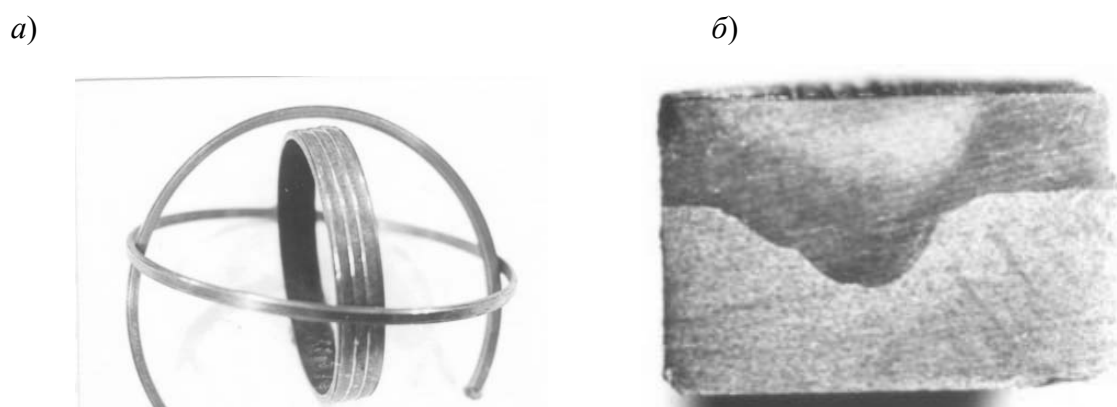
Внешний вид заготовки после электронно-лучевой наплавки бронзы БрХ08 (а) и макрошлиф полученного соединения бронзы со сталью (б)
